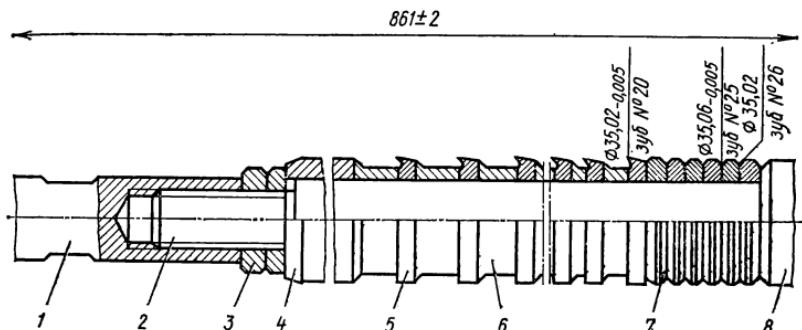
Протяжка круглая сборная твердосплавная с выглаживающими зубьями
